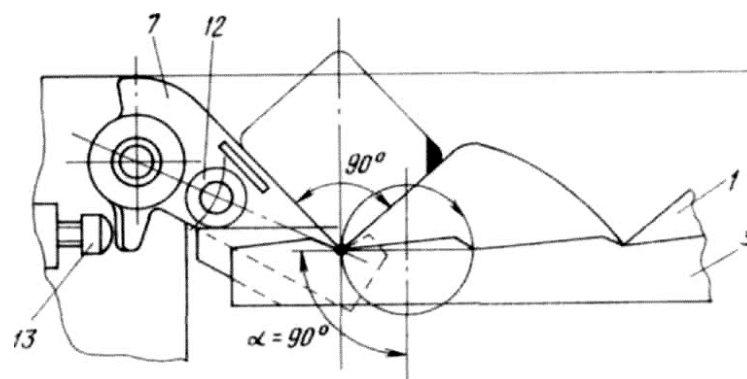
Механізм у момент опускання заготовлі на поверхню зуба опорних рейок [6]
